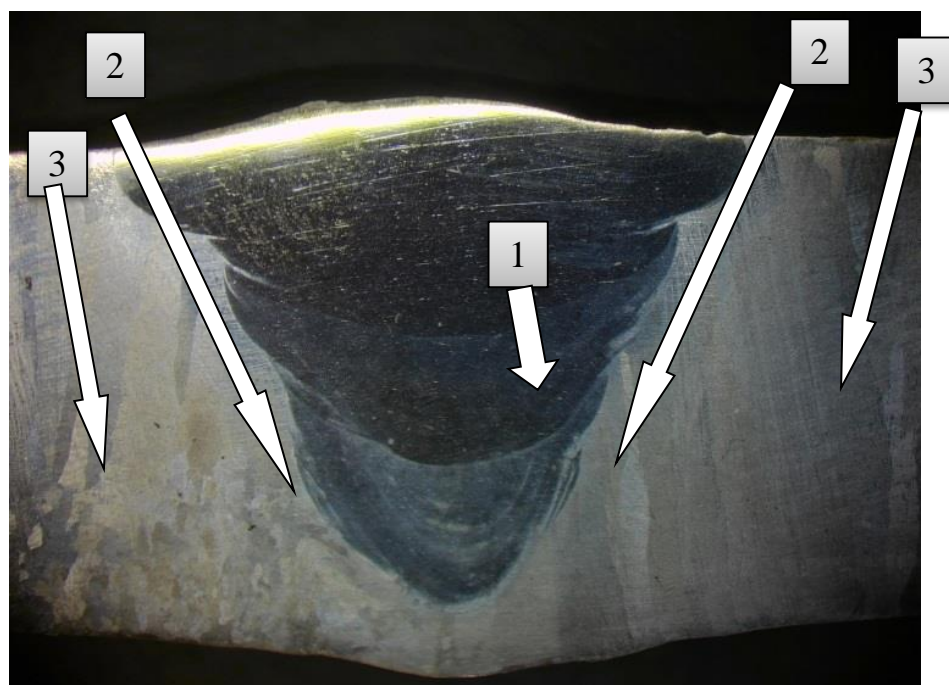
Схема разделения сварного шва на участки
